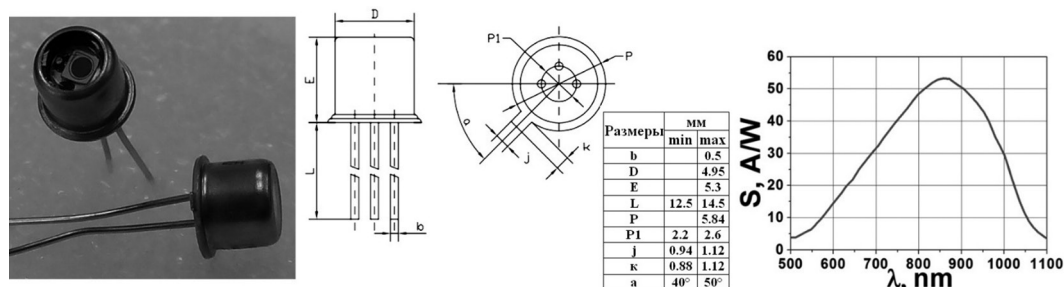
Внешний вид ЛФД в корпусе КТ-1-7 и типоразмеры
